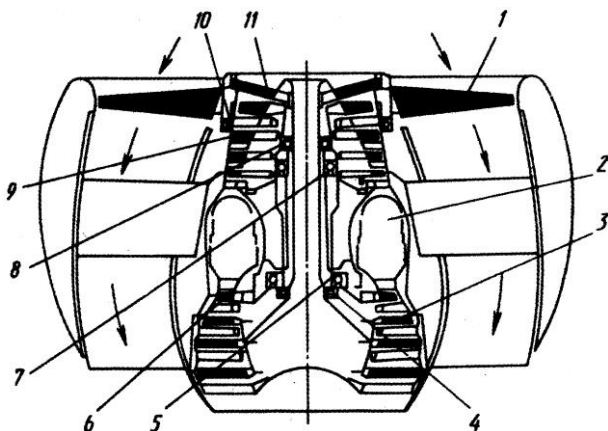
Подъемный двухконтурный турбореактивный двигатель:
